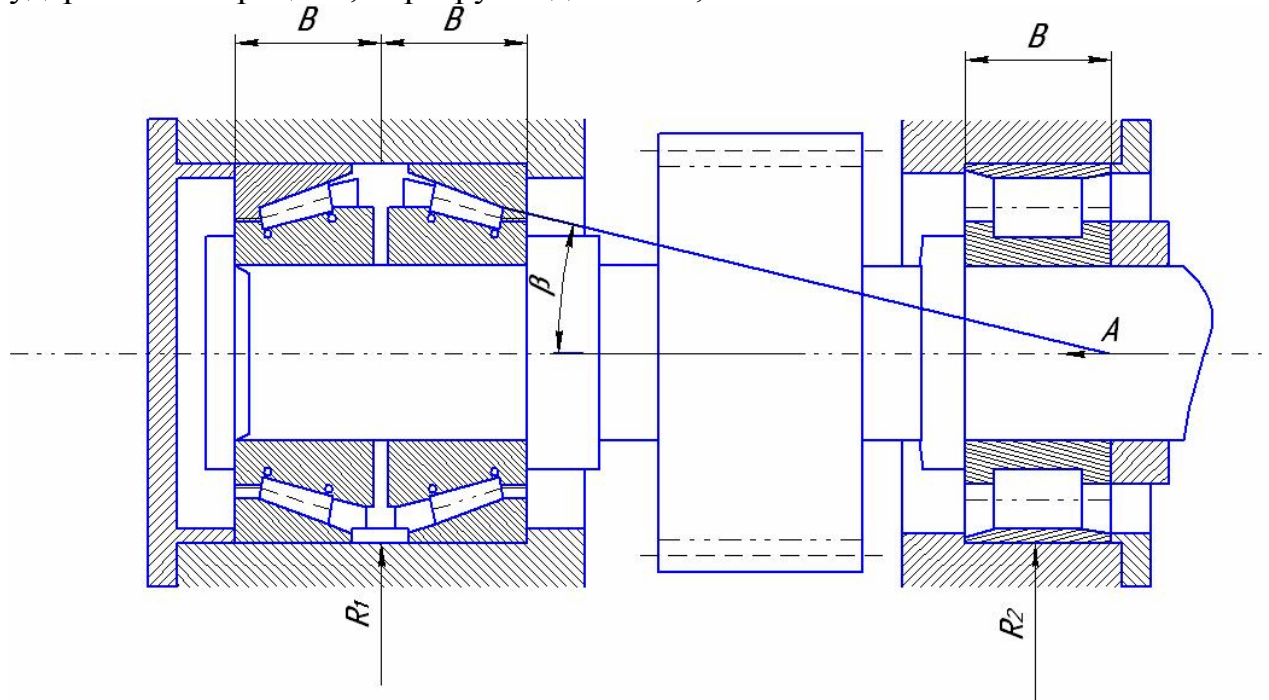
Схема установки конического роликоподшипника в фиксированной опоре вала
